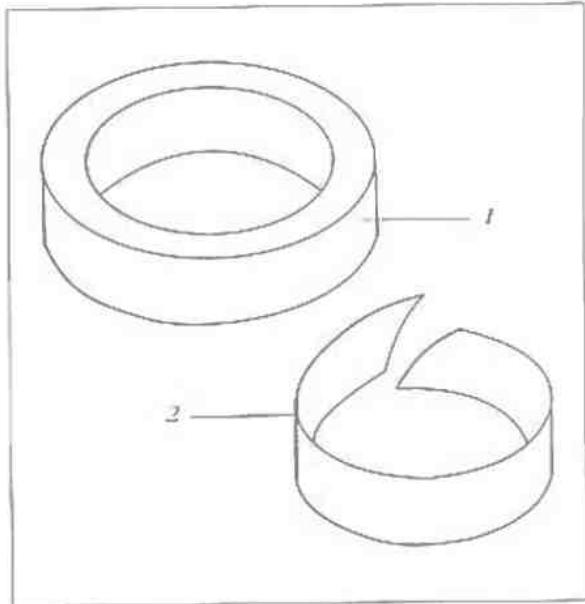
Подготовка шаблона внутренней накладки для браслета: 1 — заготовка браслета; 2 — шаблон из плотной бумаги
